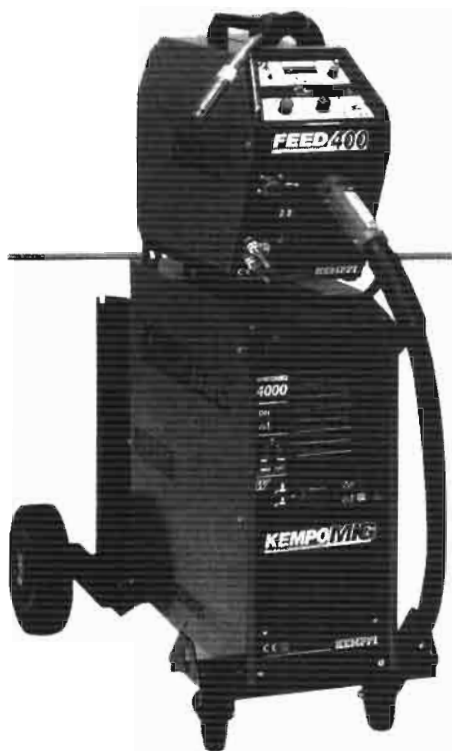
Сварочный инвертор «Кемро MIG 4000 W» с водяным охлаждением
